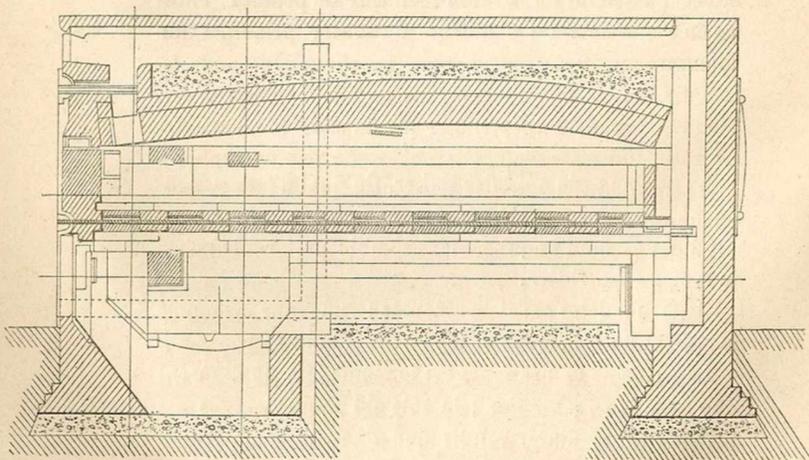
Four Bailey-Baker (Coupe longitudinale).
